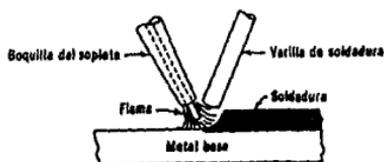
Soldadura Oxiacetilénica.
